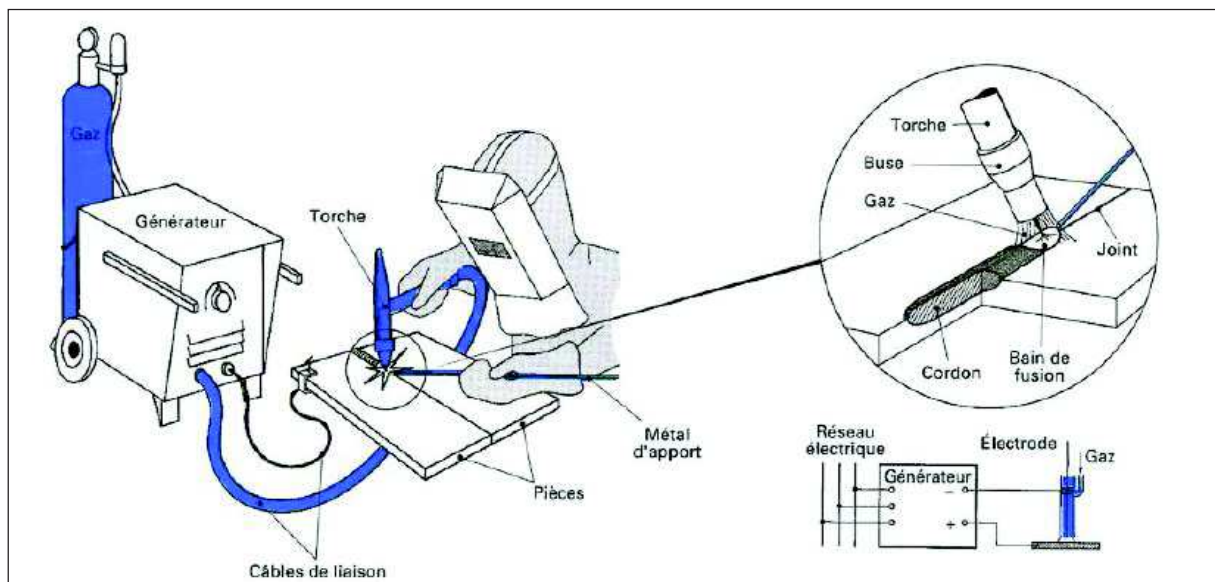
Principe du procédé de soudage GTAW [Cazes1995]
